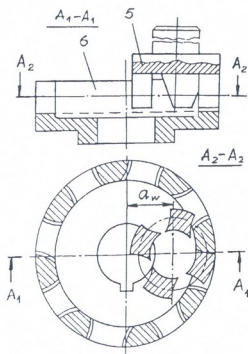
Торцевая зубчатая передача с круглыми колесами
